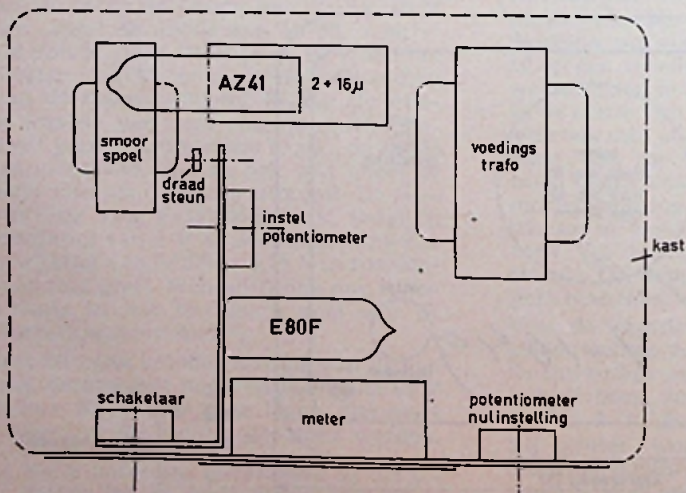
Montagevoorbeeld in bovenaanzicht
